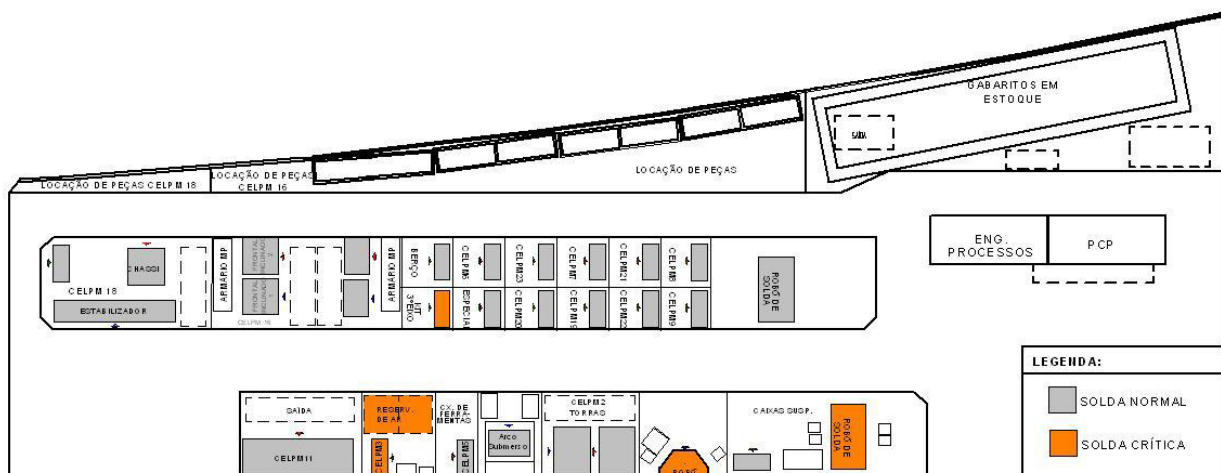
Layout do Setor da Pré-Montagem. Fonte: Empresa em estudo (2011).
